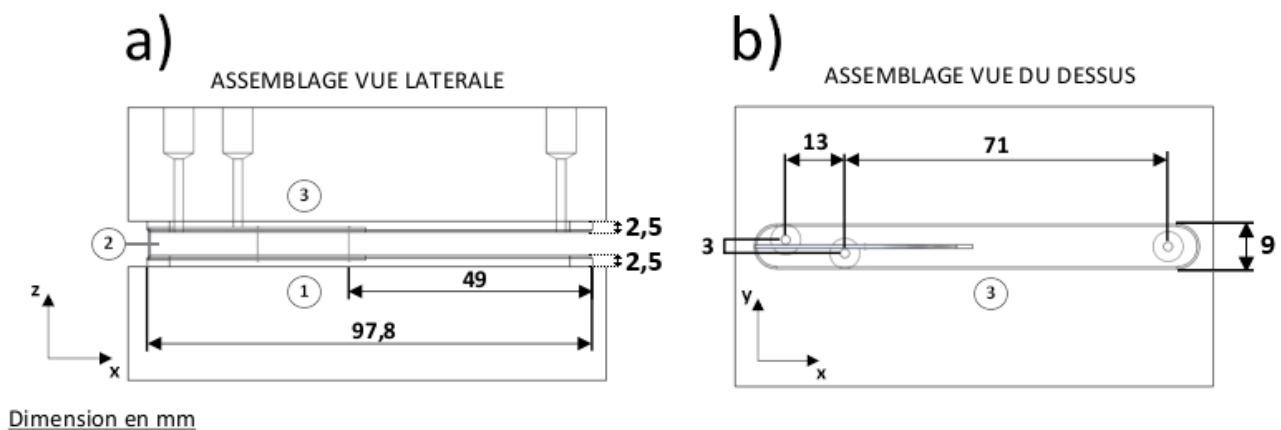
Dessins techniques 2D (à l'échelle) du montage du canal ultrasonore sans la sonotrode avec certaines dimensions caractéristiques sur la vue latérale (a) et sur la vue du dessus (b), 1 : couvercle inférieur, 2 : plaque de séparation, 3 : couvercle supérieur. (Les trous pour les 10 vis ont été cachés volontairement pour une meilleure lisibilité.)
